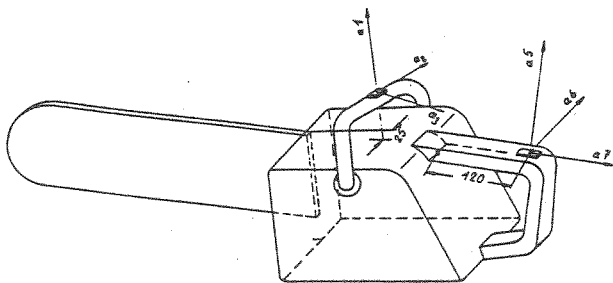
Skizze Motorsäge mit Beschleunigungsaufnehmer
